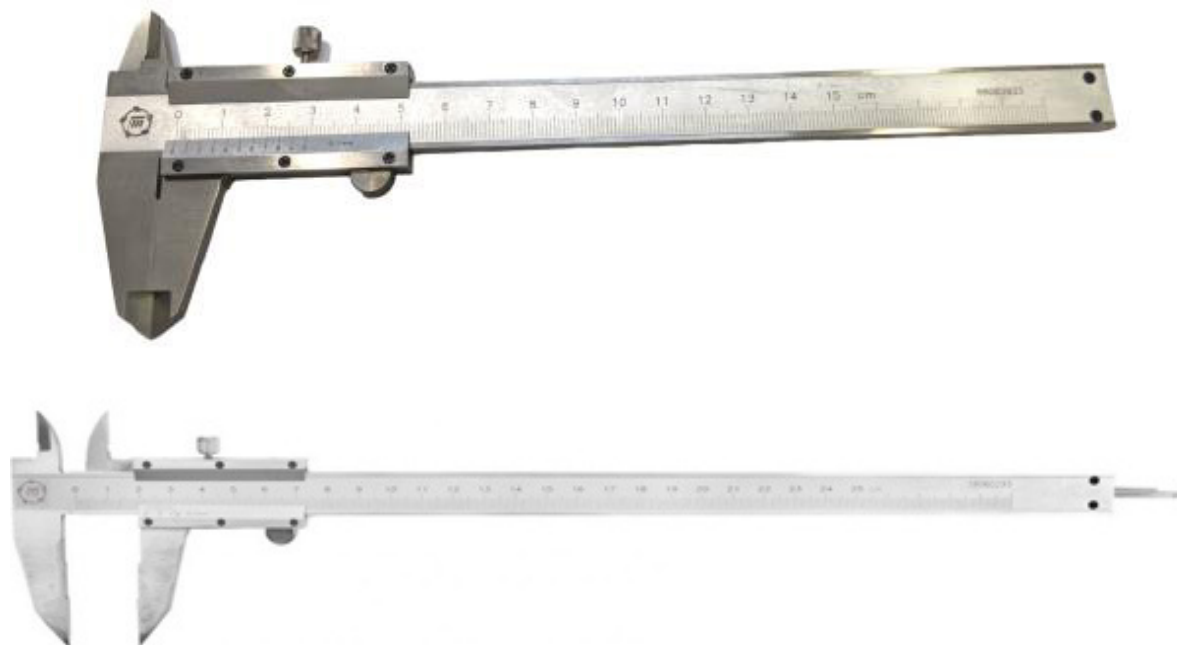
Общий вид штангенциркулей ШЦ типа I
